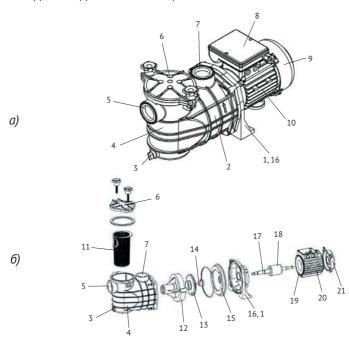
JET POOL HCP а) – общий вид; б) – конструкция
